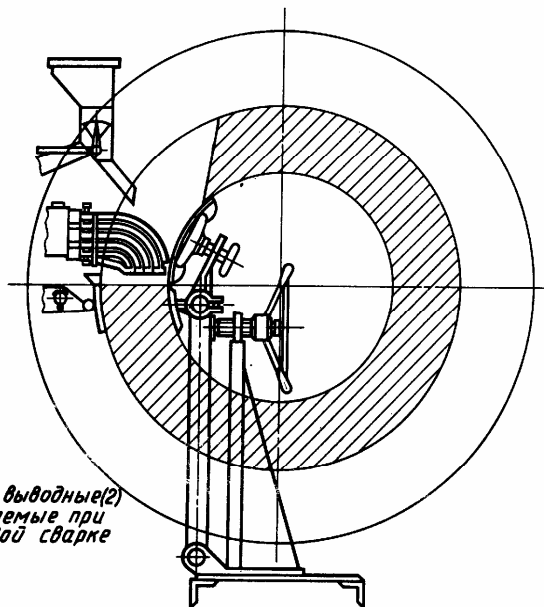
Сварка вала с применением внутреннего ползуна
